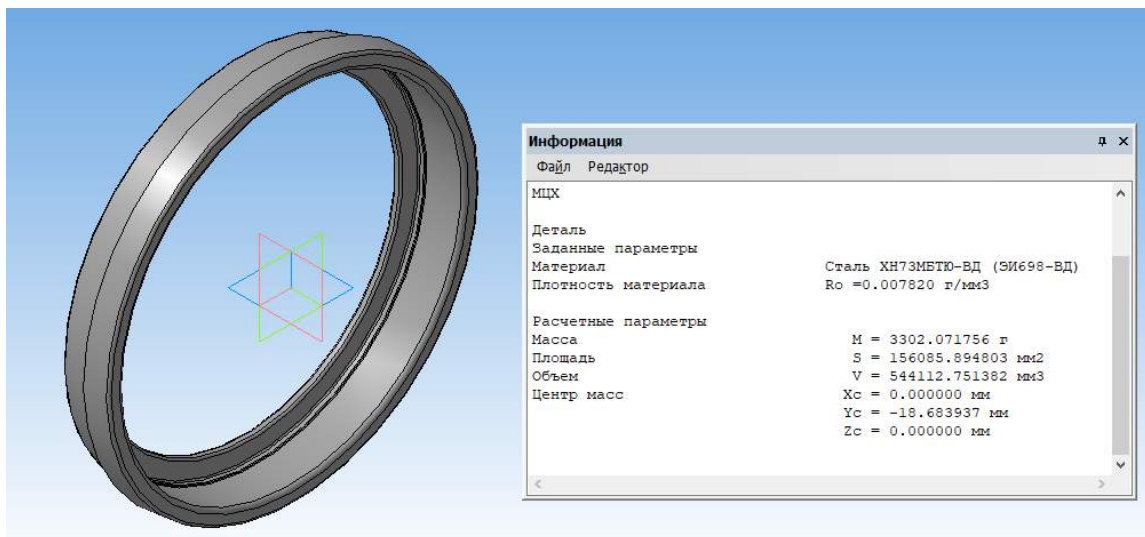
3D модель штампованої заготовки на ГКМ
